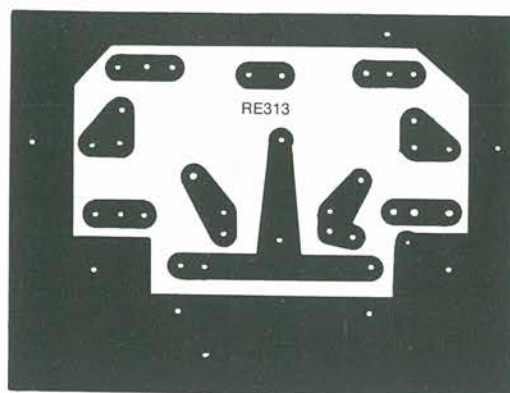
Circuito stampato scala 1:1 per il montaggio dei trimmer R5-R6.
